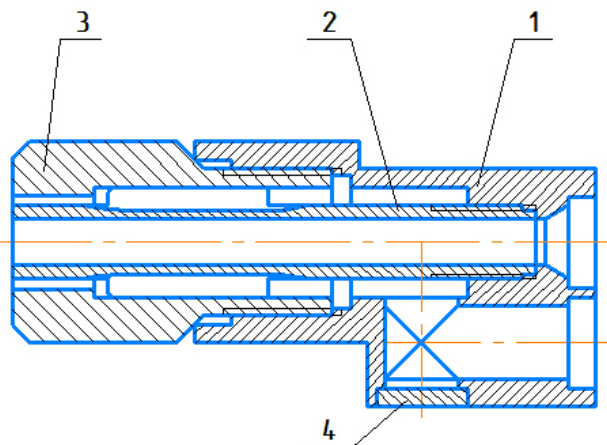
Головка в сборе резака РЗ-ФЛЦ
